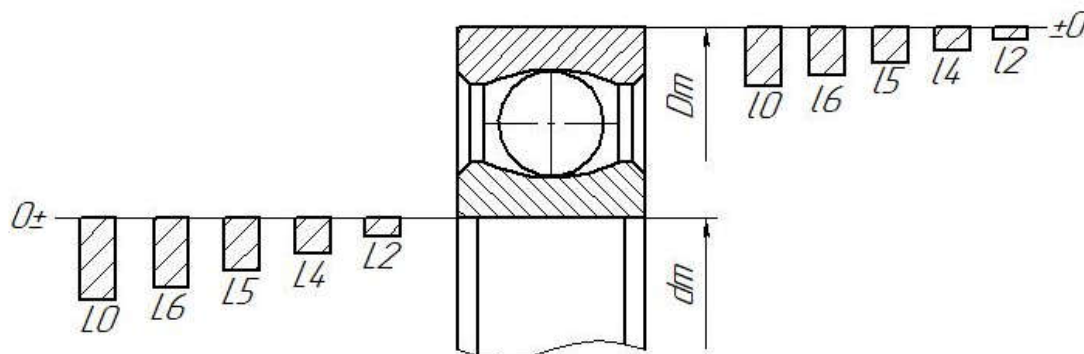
Схема расположения интервалов допусков на средние наружный диаметр и внутренний диаметр подшипников по классам точности
